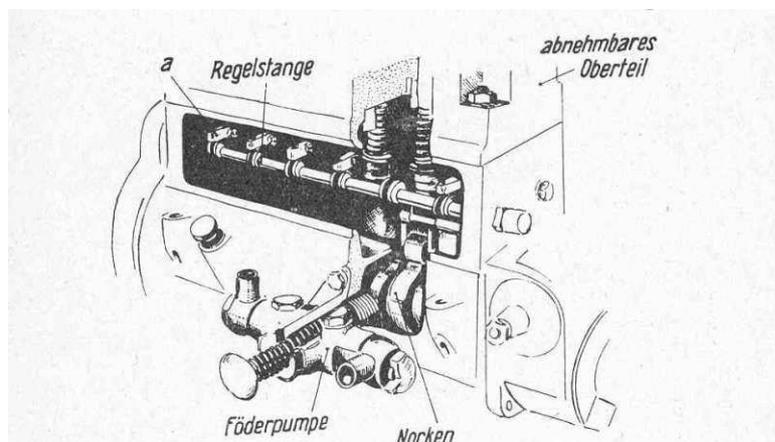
Deckel PRA Pumpe, seitliche Ansicht
